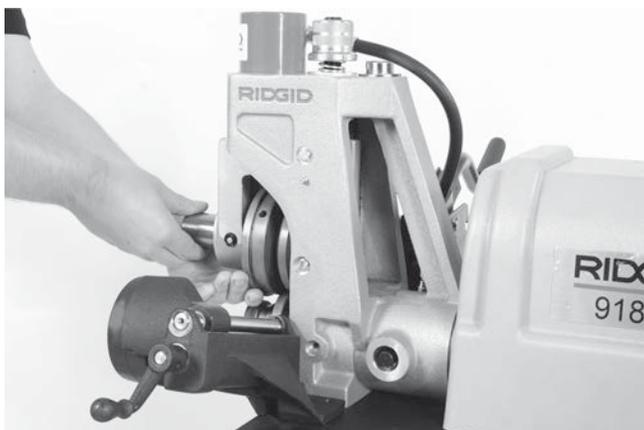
Снятие удерживающего вала и накатывающего ролика
